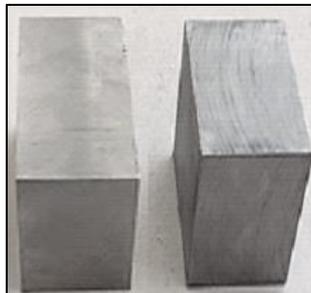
Образцы для высокоскоростного фрезерования из стали 15X12BMФ
